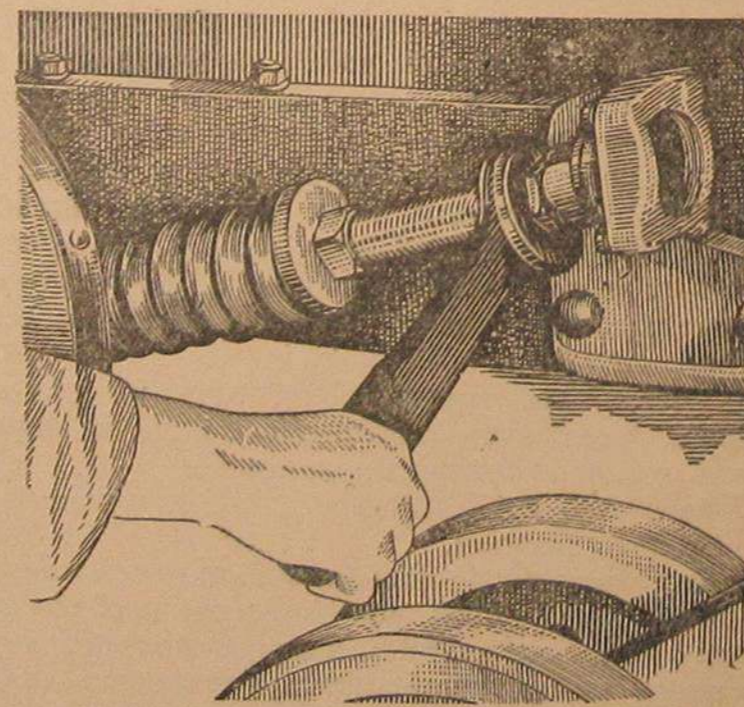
Регулировка конических подшипников направляющего колеса.
